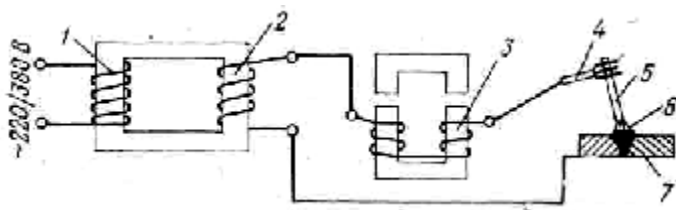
Схема установки для дуговой сварки переменным током:
